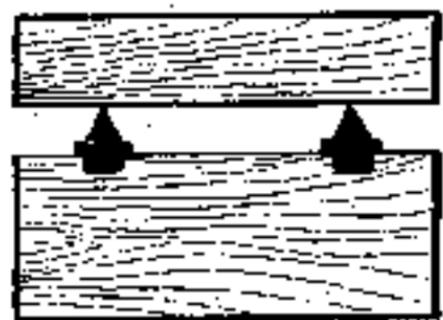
Разметка отверстий под круглые шпильки центризмк.
